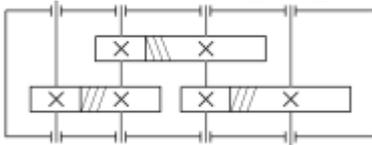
Кинематическая схема трехступенчатого цилиндрического зубчатого редуктора
